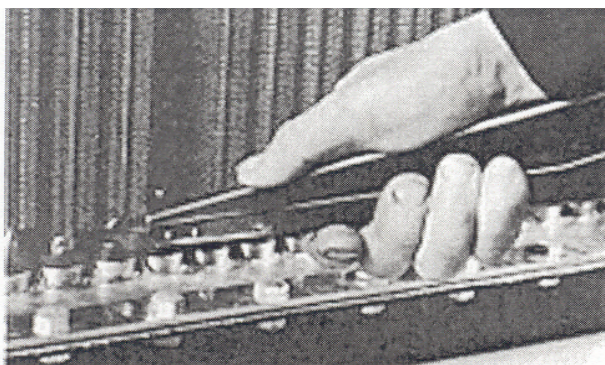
USO DE LA HERRAMIENTA DE MONTAJE PARA INSTALAR EL TUBO
